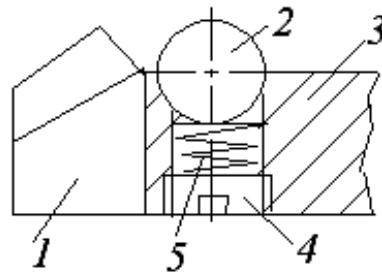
Принципиальная схема комбинированного инструмента:
